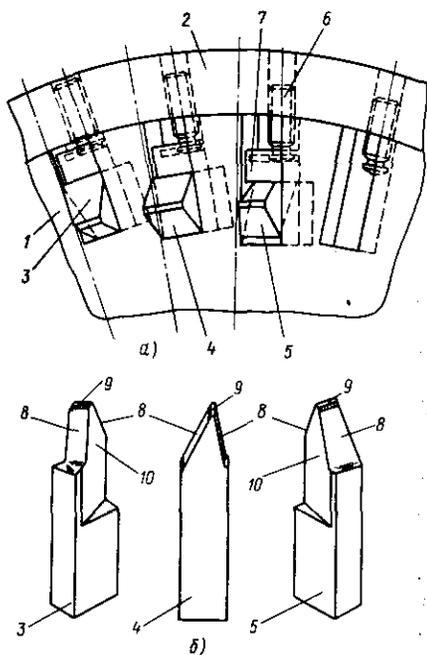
Схема установки острозаточенных резцов в корпусе (а) и конструкции резцов (б)
